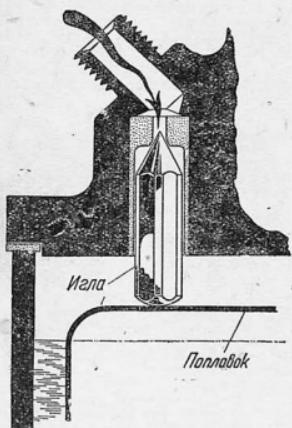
Игольчатый клапан поплавковой камеры карбюратора
